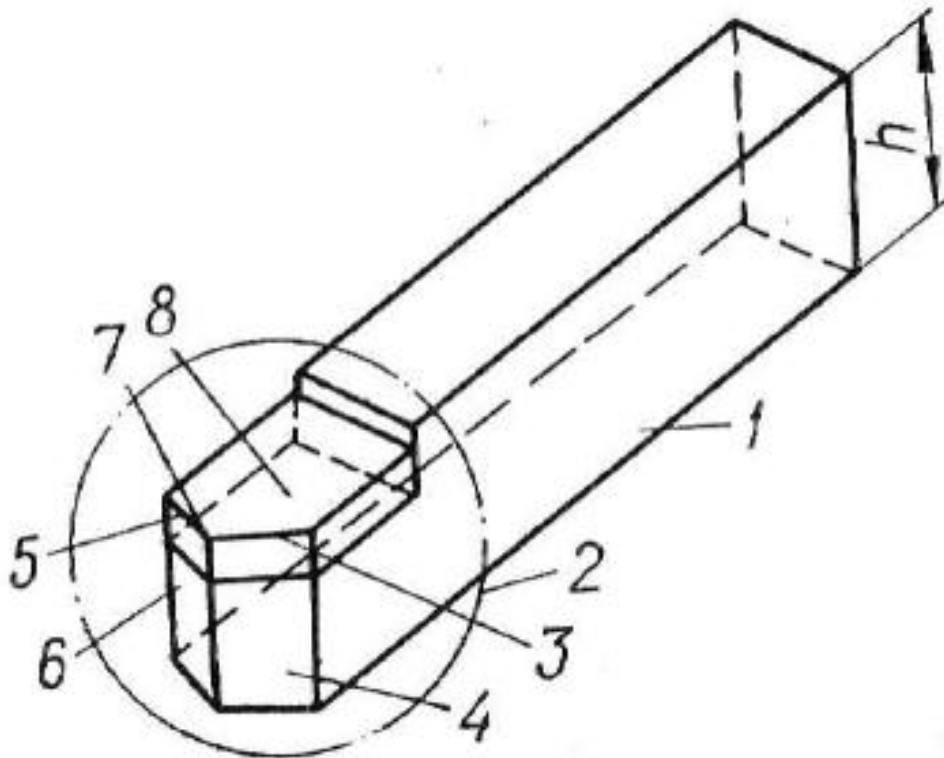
Токарний прохідний різець: 1 – стержень; 2 – головка; 3 – головна різальна кромка; 4, 6 – задні поверхні; 5 – допоміжна різальна кромка; 7 – вершина різця; 8 – передня поверхня
